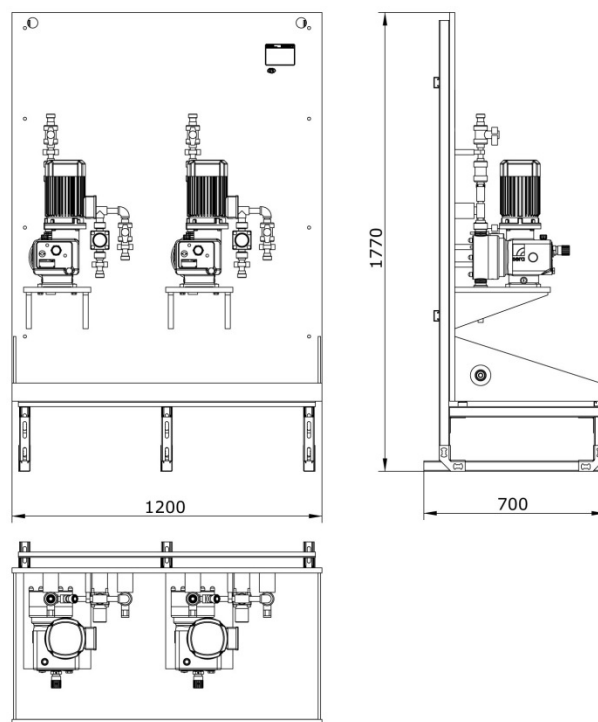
Dimensions CVD 2 (montage au sol, châssis acier)
